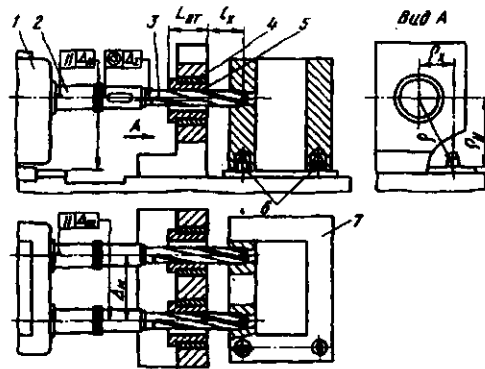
Схема обработки отверстий жестко закрепленным инструментом с направлением: 1 - агрегатная головка; 2 - шпиндель станка; 3 - инструментальная наладка; 4 - постоянная кондукторная втулка; 5 - сменная кондукторная втулка; 6 - установочные пальцы; 7 - обрабатываемая заготовка; R_x, R_y, R - параметры расположения оси шпинделя станка относительно базовых элементов позиции
